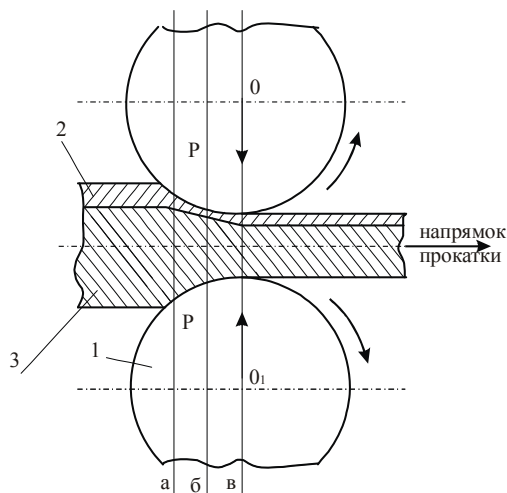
Схема прокатки біметалу із двошарового пакета (пояснення позначень наведені в тексті): 1- валки; 2 - плакуючий шар (пласт); 3 - основний шар.
